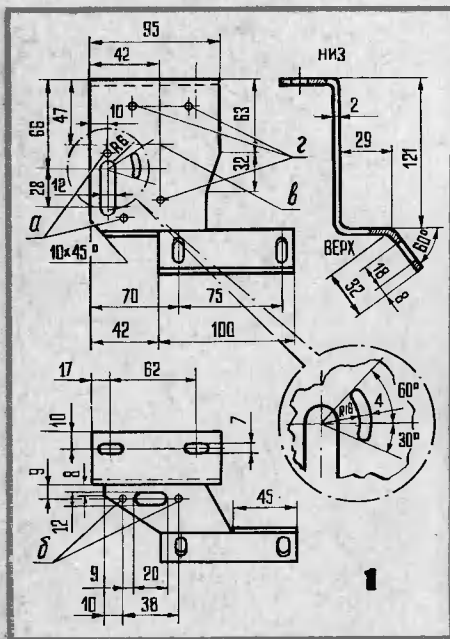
Кронштейн: а — отверстия М4 для крепления сопротивления (сверлить по месту); б — два отверстия (диаметром 4,1) крепления предохранителя; в — центр крепления редуктора; г — три отверстия (диаметром 5,1) крепления редуктора.
